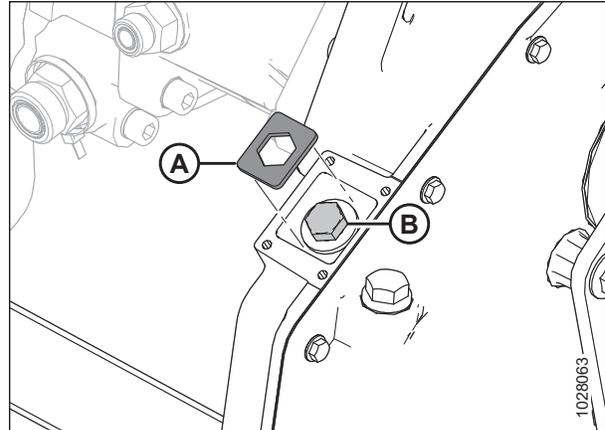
Hauptgetriebe mit Kettenspanner
